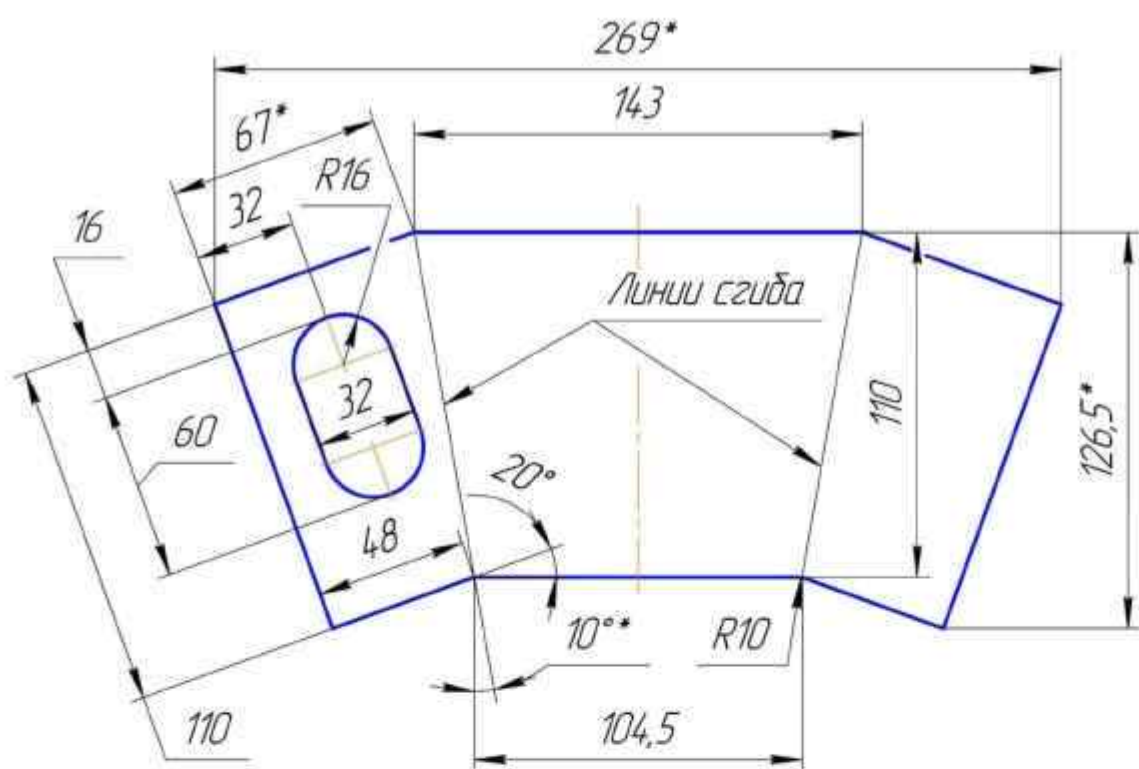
Развертка лотка направляющего КФ-106.04.01.008
